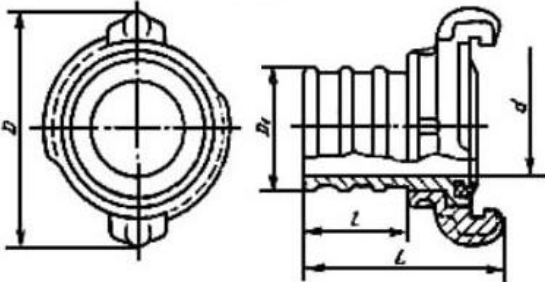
Общий вид крепления разработанного устройства на соединительную головку
